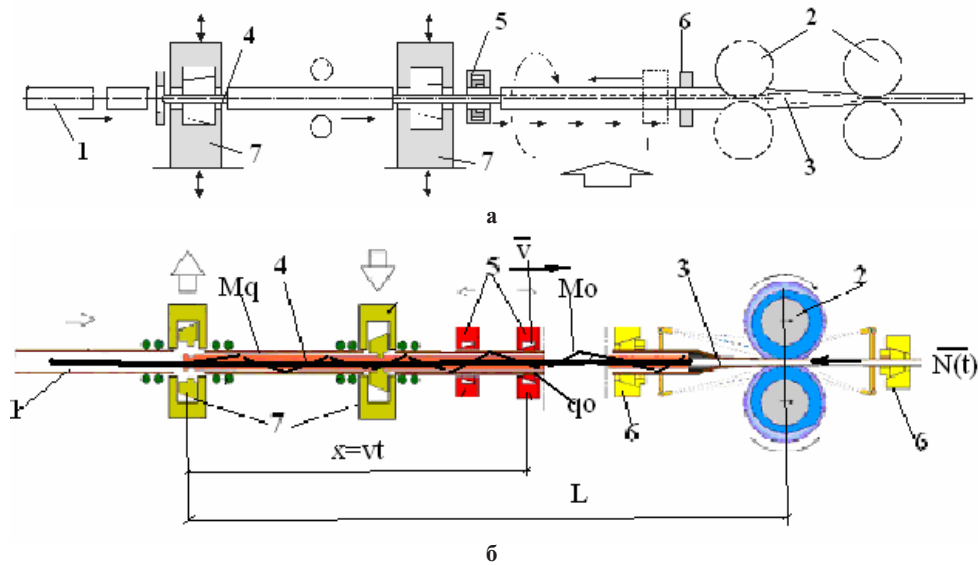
Стан холодной пильгерной прокатки труб с осевой загрузкой трубных заготовок и расчетная схема механизма удержания оправки стана ХПТ б): 1 – трубная заготовка (гильза); 2 – валки рабочие; 3 – оправка; 4 – стержень оправки; 5 – патроны подачи трубы; 6 – патроны поворота трубы; 7 – патроны удержания стержня оправки
